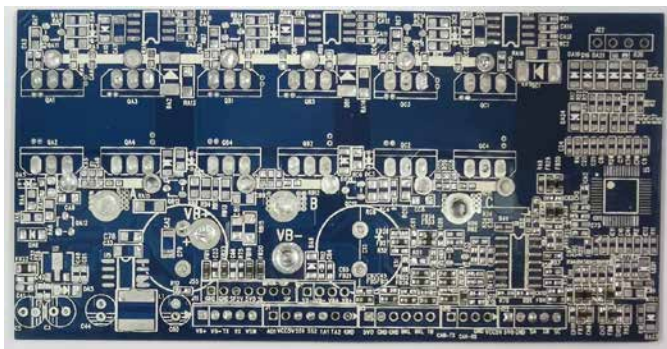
Zeigt den Top-Layer des PCBs (Printed Circuit Board), wo alle Komponenten entfernt wurden.
